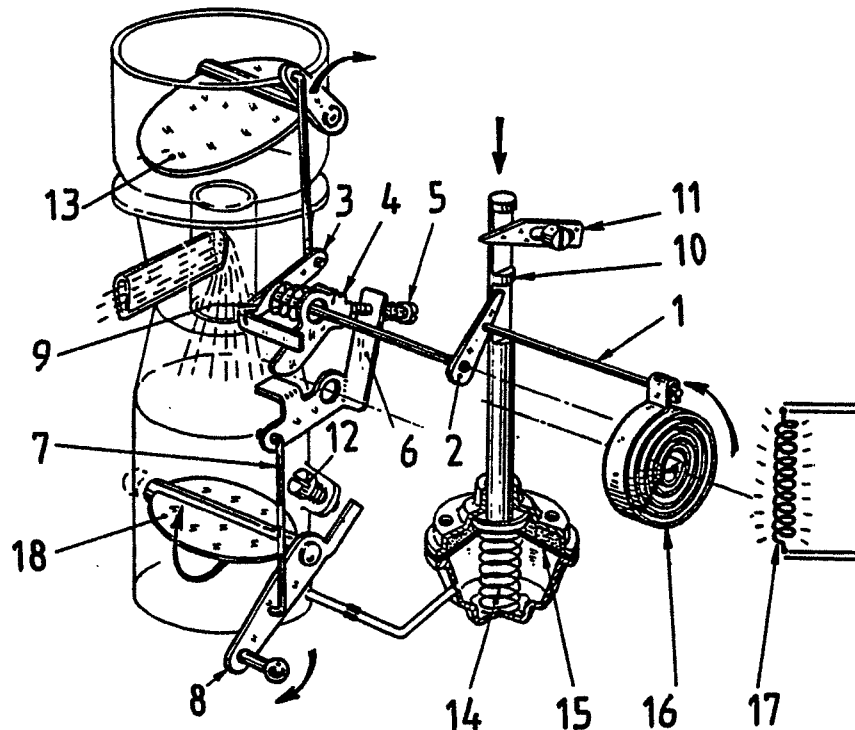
[2] — Carburatore munito di starter automatico.
